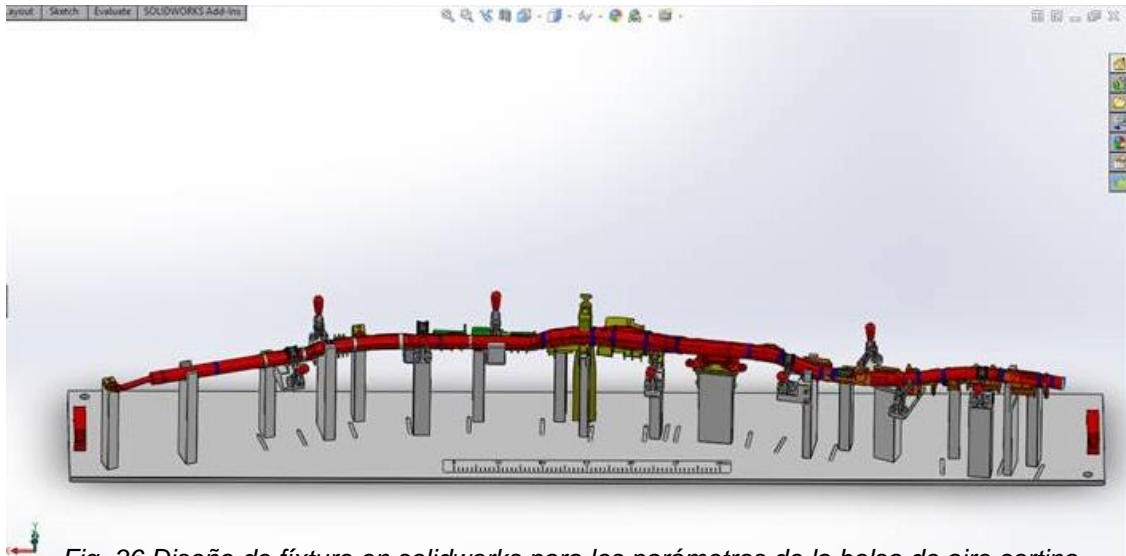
Diseño de fixture en solidworks para los parámetros de la bolsa de aire cortina
